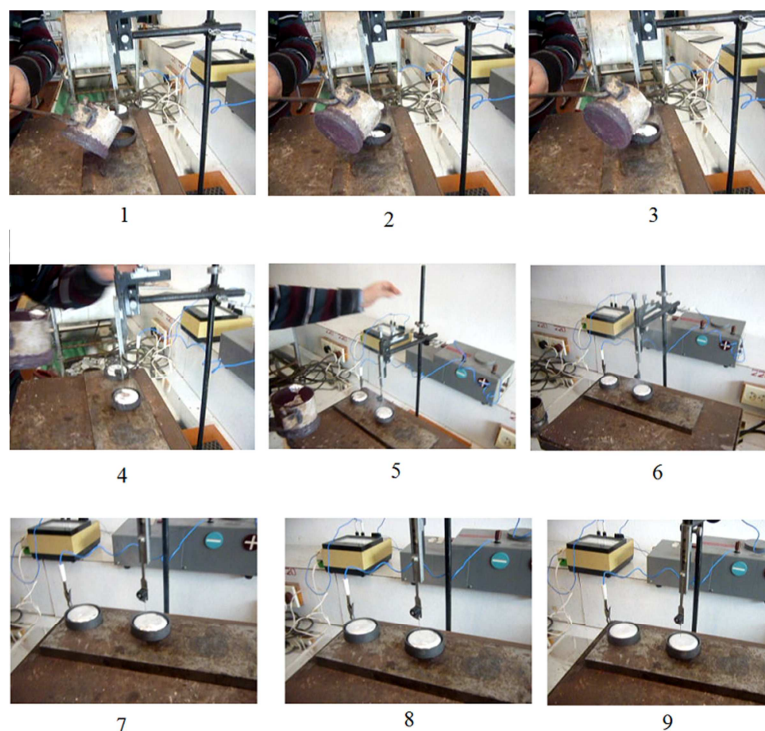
Динамика отливки и обработки образцов коронным разрядом. На 1 по 9 кадр - справа отливка К слева отливка М.
